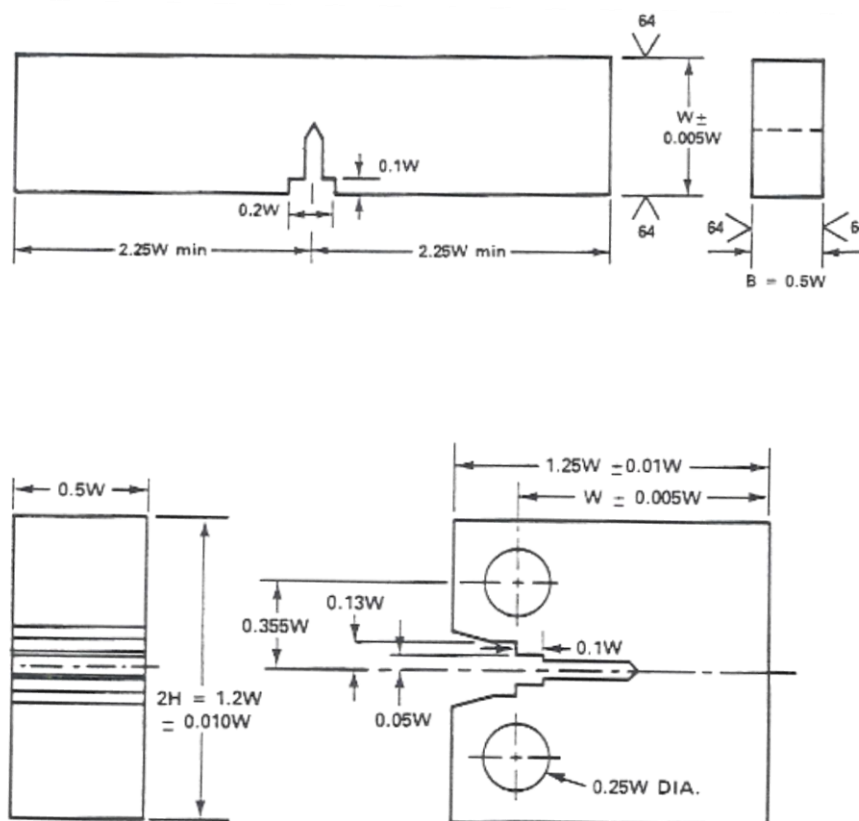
Ensaios para caracterização da propagação de fissuras (QUARESMA, 1992).
